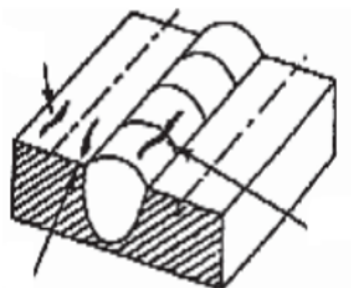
Эскиз дефекта сварного шва
